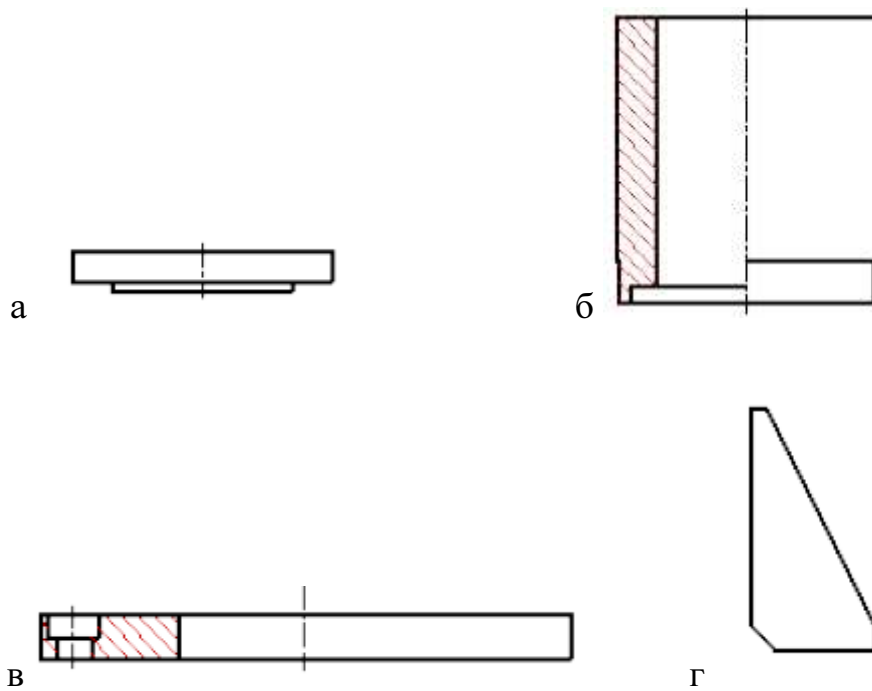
Эскизы деталей, входящих в сварную сборочную единицу:
